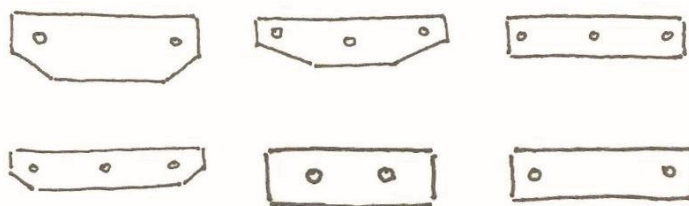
najčastejšie využívané tvary fixačných štítkov spony
